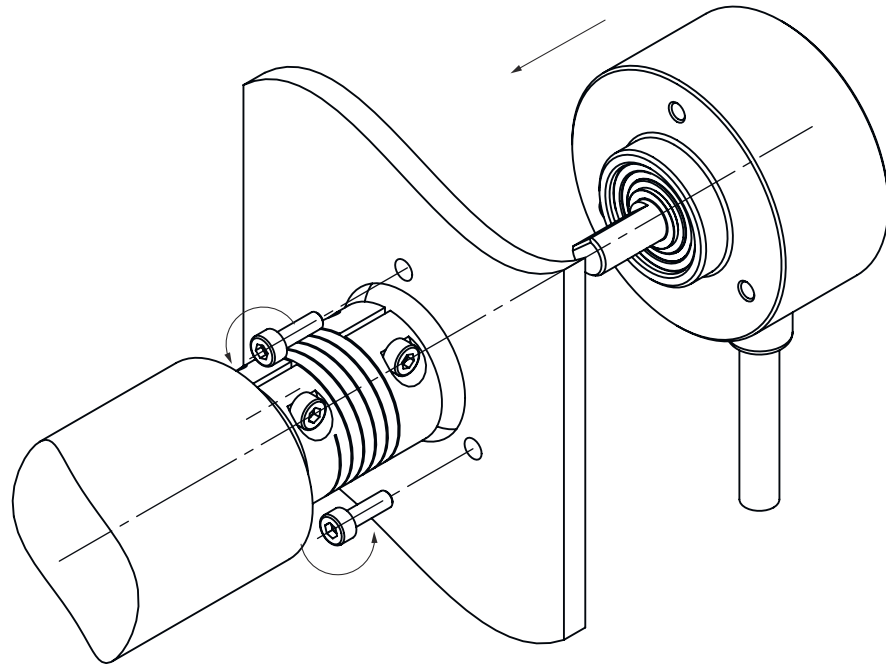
Anbau über flanschseitige Gewindebohrungen
